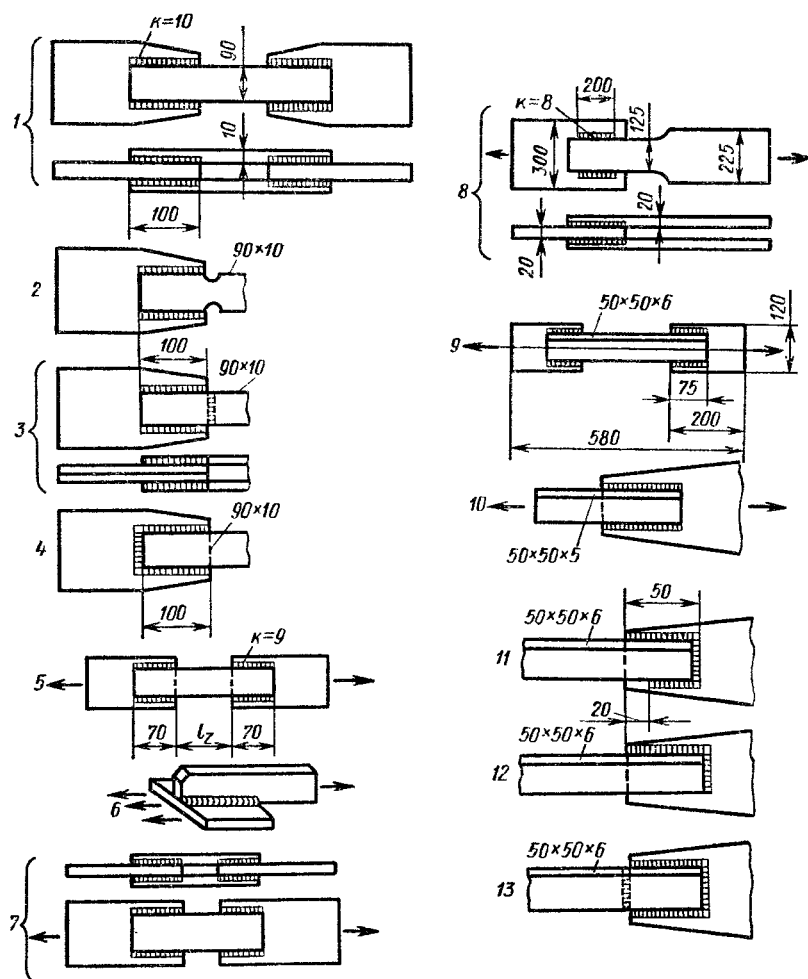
Эскизы образцов соединений с фланговыми швами для испытания на усталость
